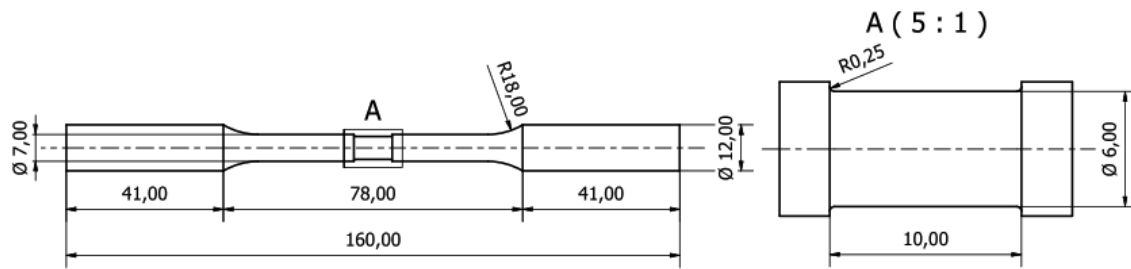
Dimensiones de probeta con ranura de fondo plano con filete
